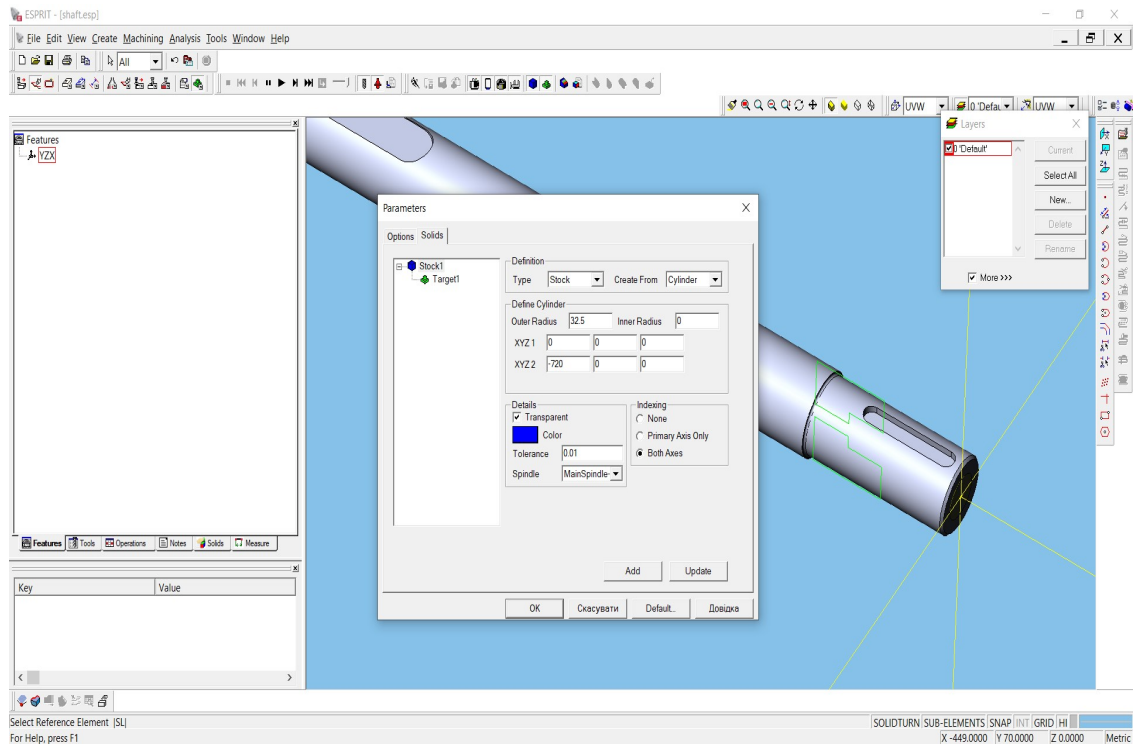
Розпізнавання елементів профілю деталі «Вал»
